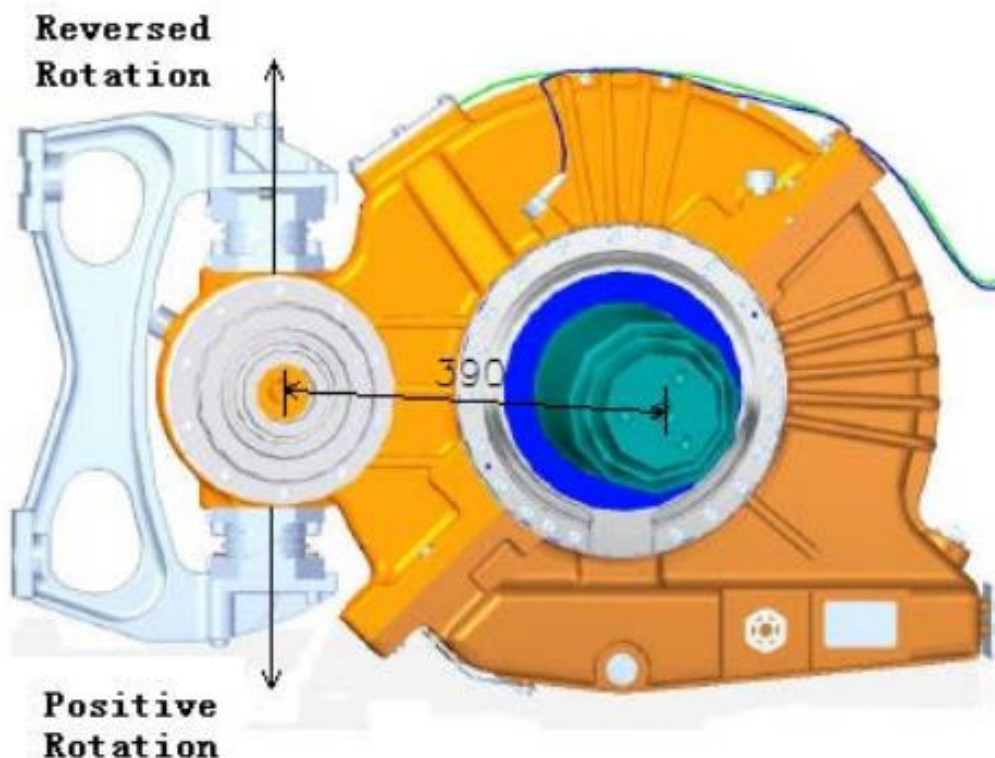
Кріплення кронштейну до корпусу редуктора
